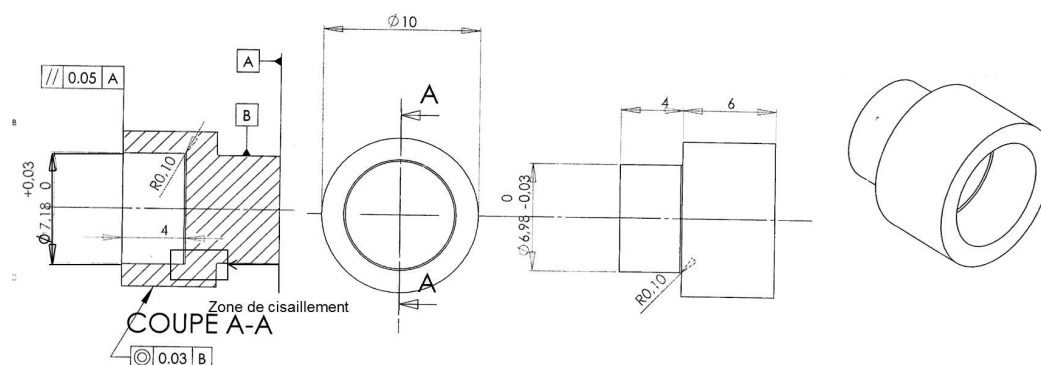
Plan des éprouvettes chapeaux (dimensions en mm).
